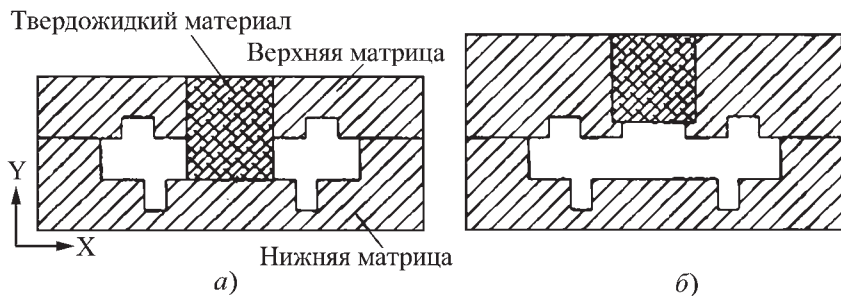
Варианты конструкций штампа с различными загрузочными камерами:
